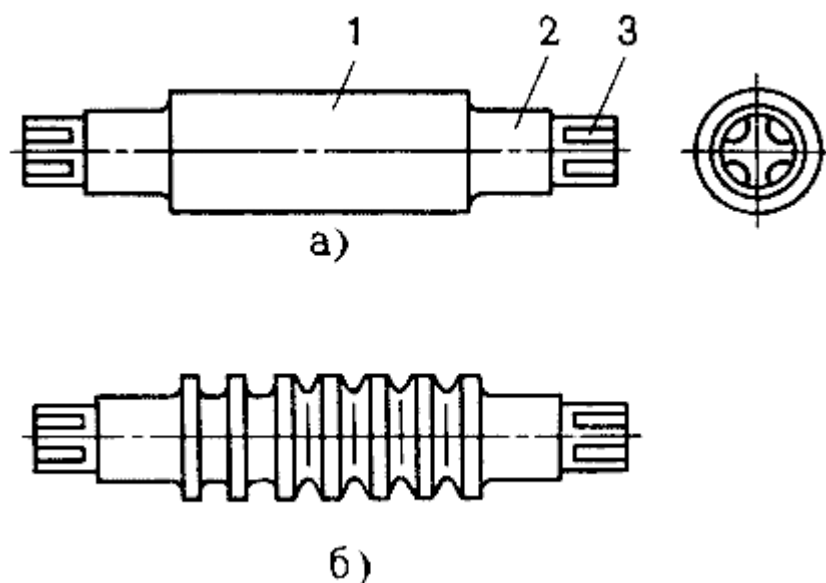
Прокатные валки: а – гладкий ; б – калиброванный
